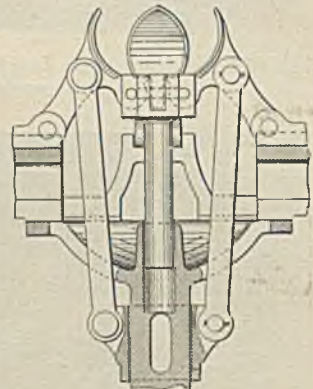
Eccles-Ballmaschine mit 4 Backen, geöffnet, im Längsschnitt
